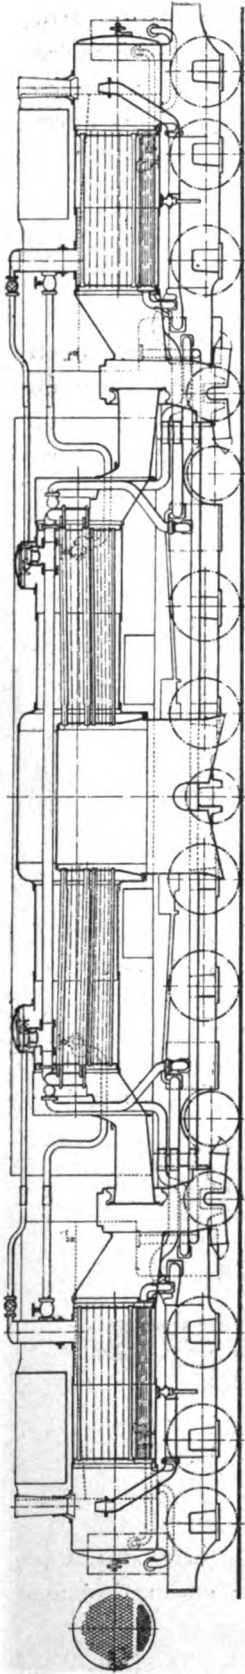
Sezione longitudinale e pianta della locomotiva Franco.
